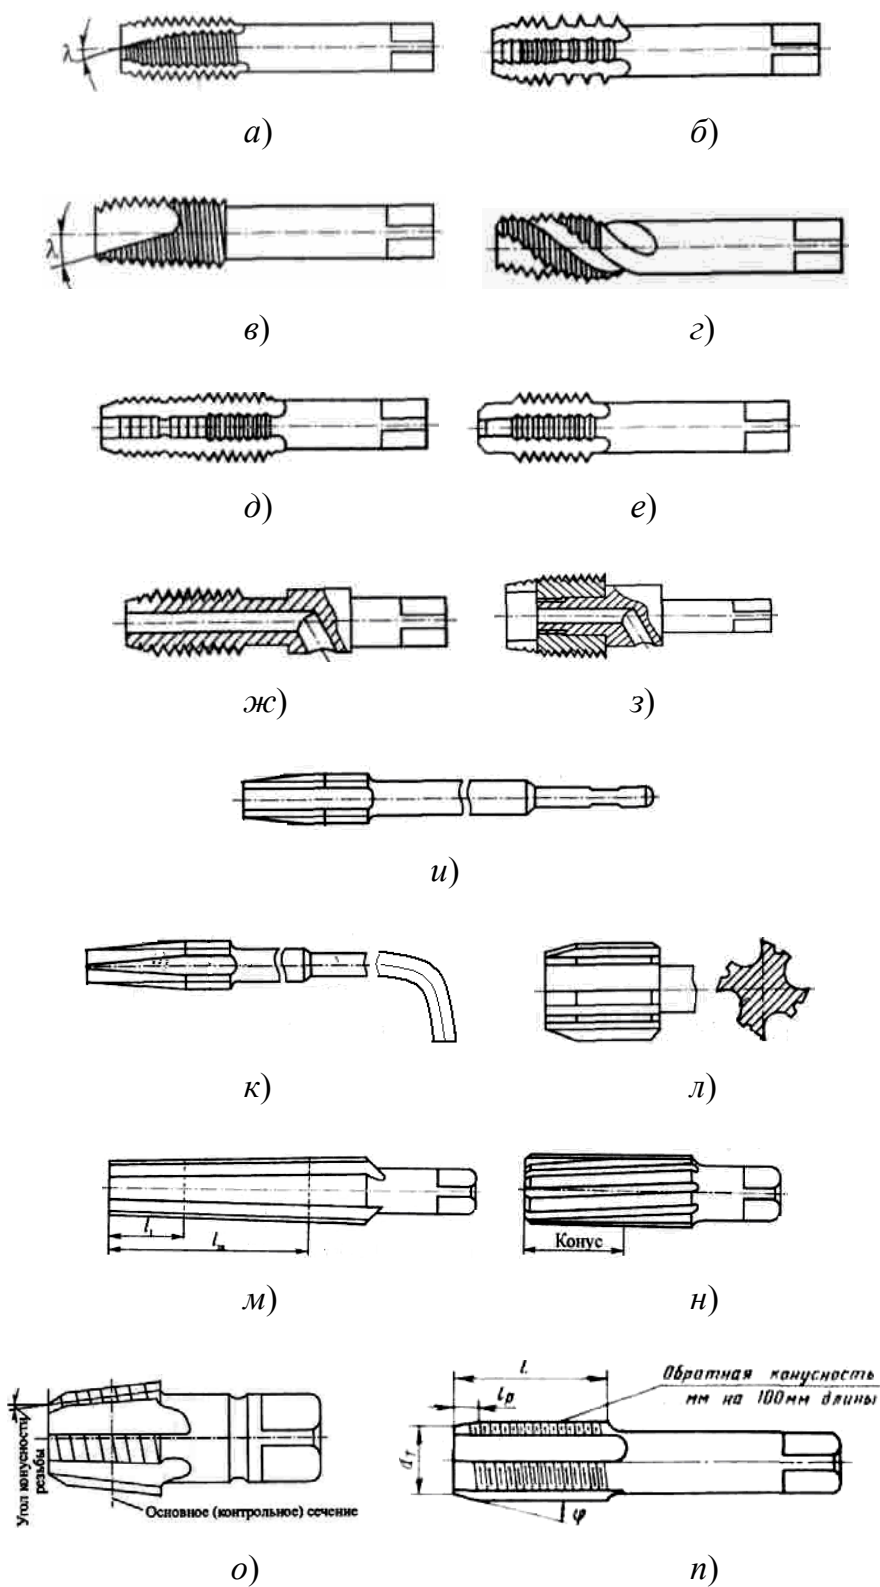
Эскизы метчиков: а – слесарный (ручной); б – с шахматным расположением зубьев; в – с укороченной канавкой; г – с винтовыми канавками; д – комбинированный; е – с передней направляющей; ж – с центральным отверстием; з – сборный; и – гаечный; к – для станков автоматов; л – режуще-выглаживающий; м – плащечный; н – маточный; о – конический; п – параметры метчика
